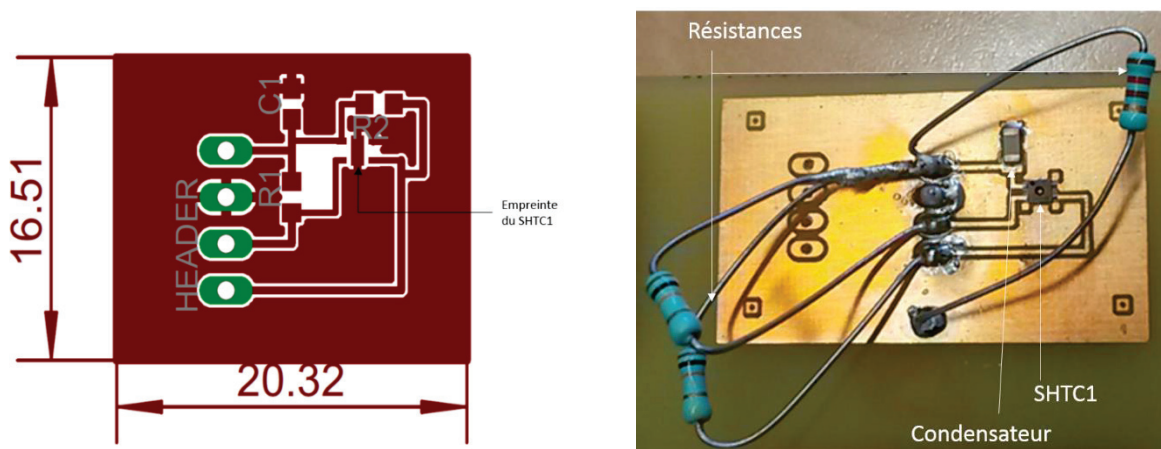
Layout de la carte conçue (dimensions en mm) et photo du PCB fabriqué avec les composants soudés
